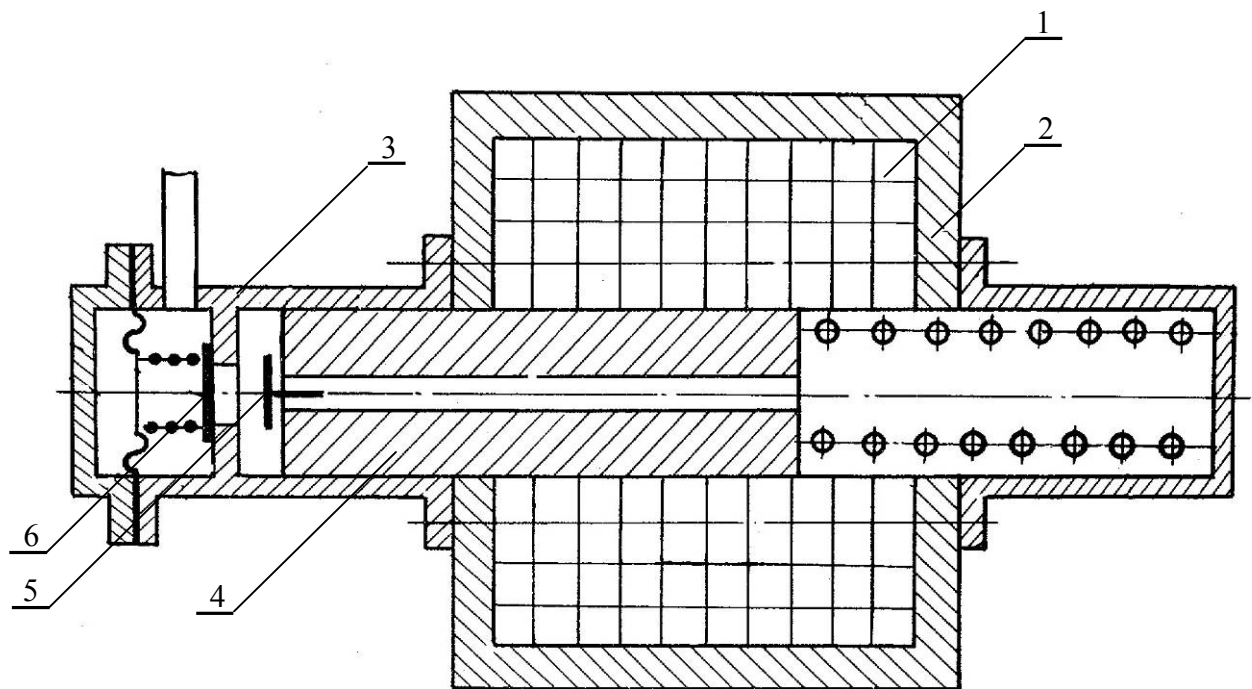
Однокатушечный электромагнитный свободнопоршневой компрессор
